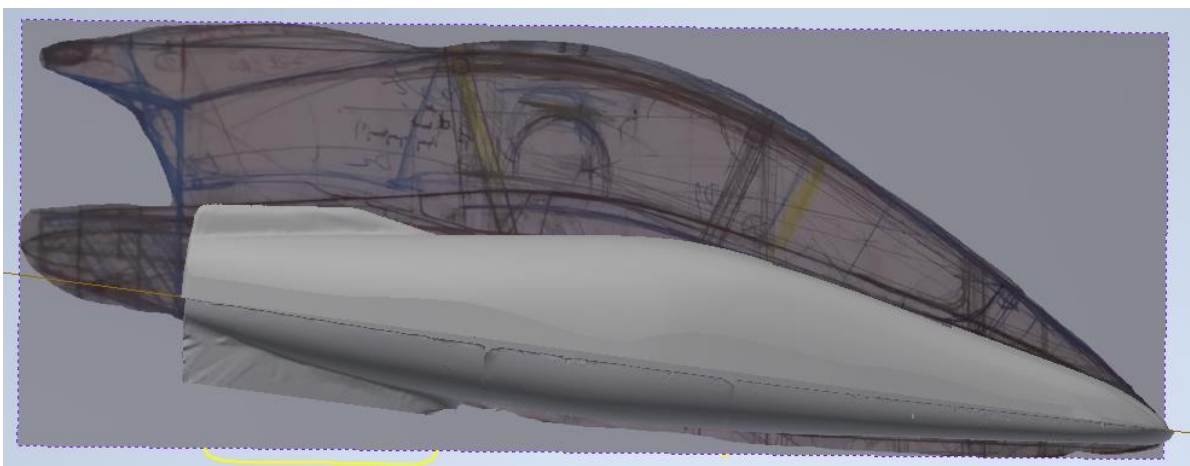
Návrhový sketch 7: Tvary odnímatelných deformačních zón
